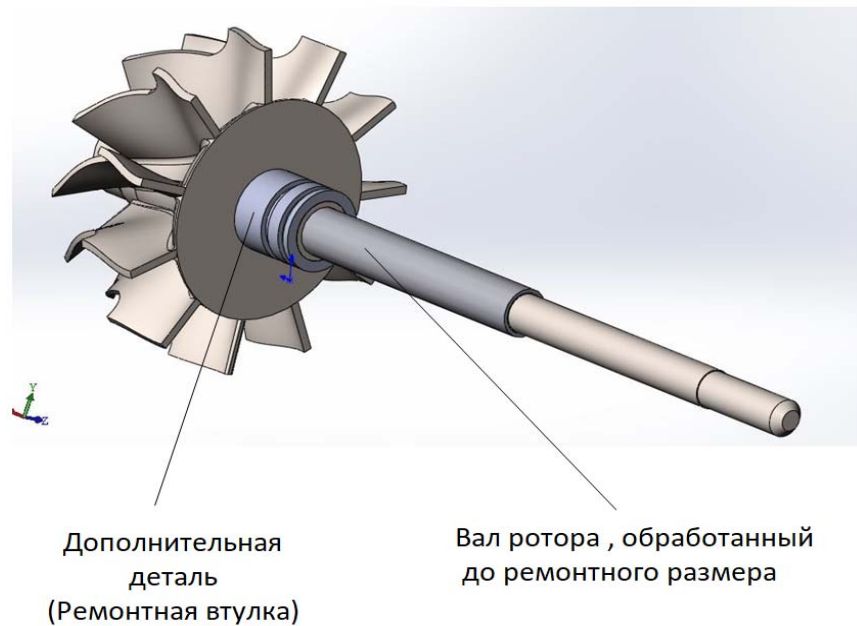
Твёрдотельная модель вала ротора турбокомпрессора с установленной дополнительной деталью
